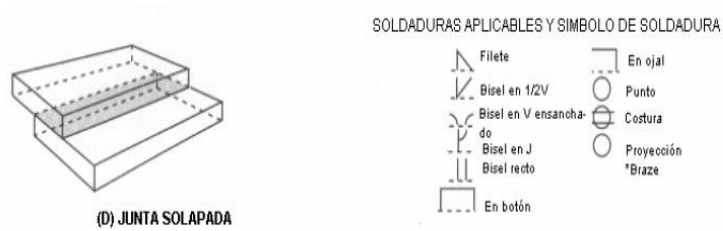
Junta solapada y la soldadura aplicable
